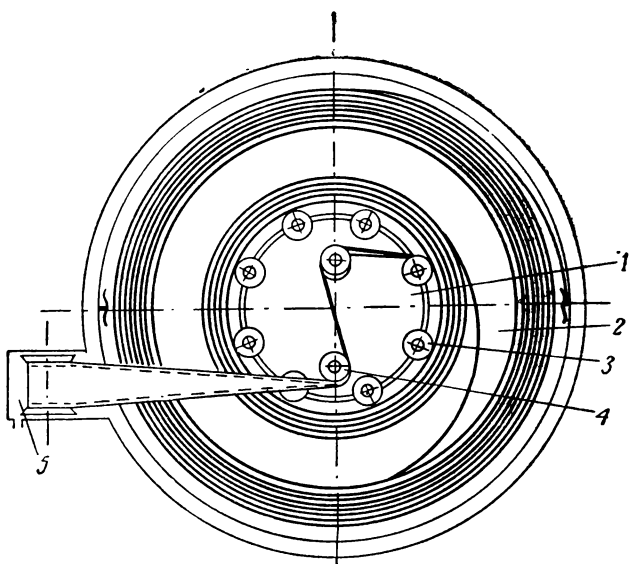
Схема прохождения фильма в разматывателе, в котором рулон размещается на вращающемся диске (вид сверху):
